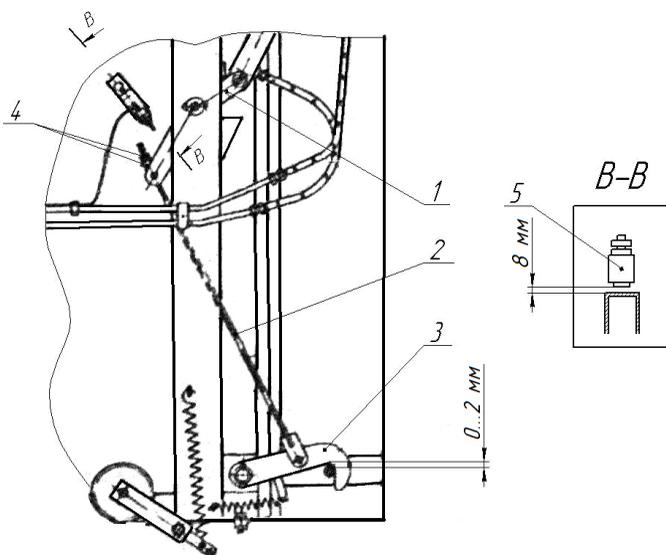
Схема регулировки натяжения механизма прессования:
